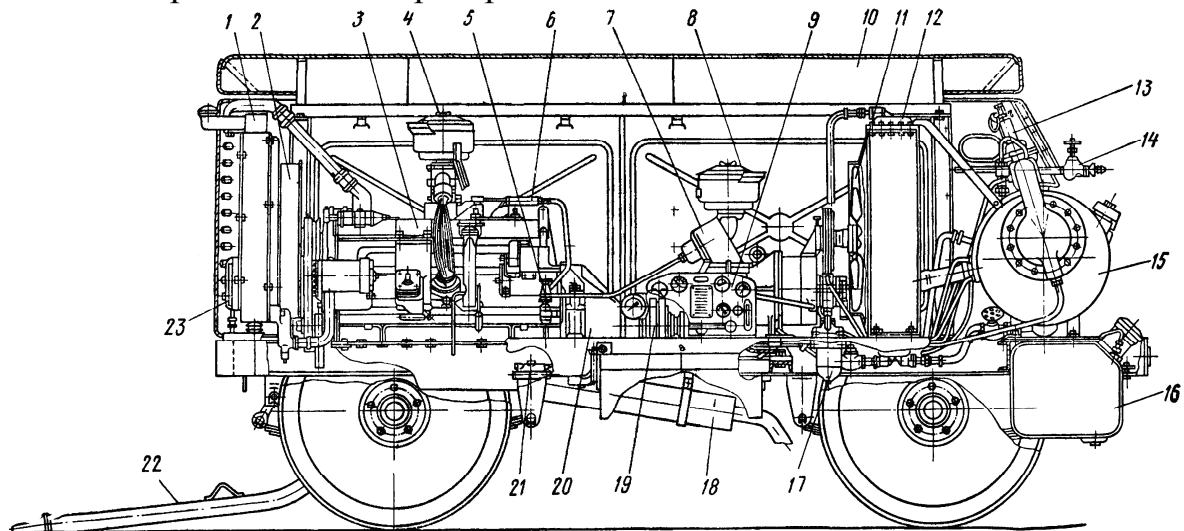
Пересувна компресорна станція ЗИФ-55В:
